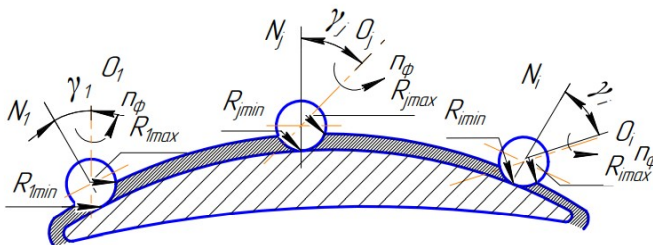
Схема положений инструмента со сферической режущей поверхностью на поверхности заготовки
